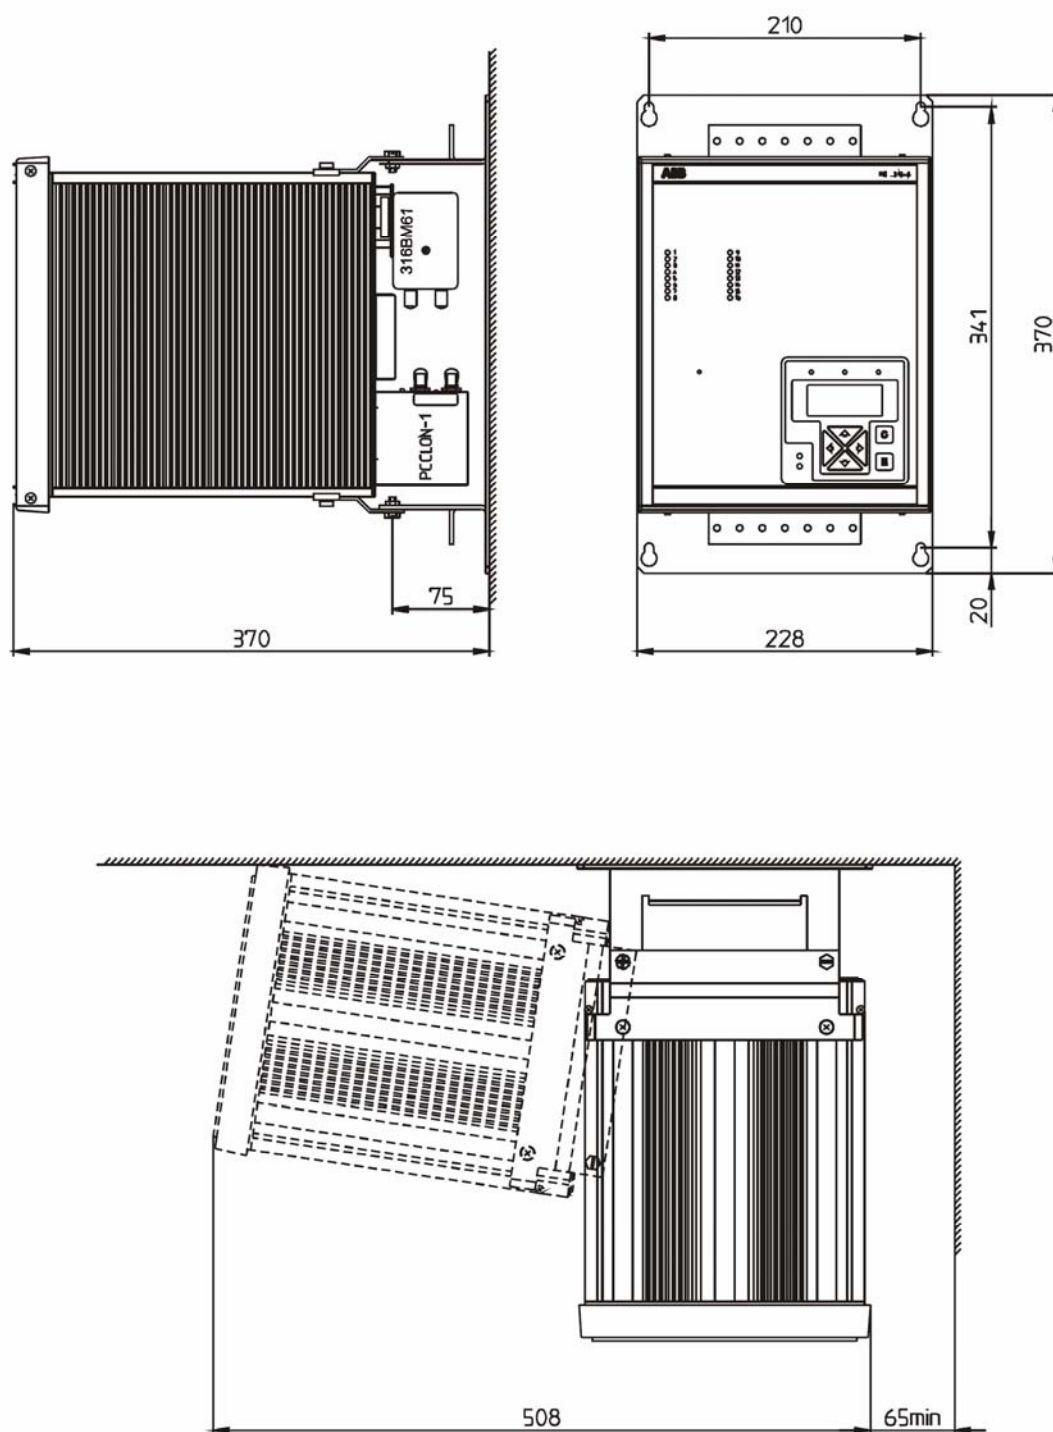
Навесной монтаж, корпус может поворачиваться влево, заднее присоединение, корпус размером N1
